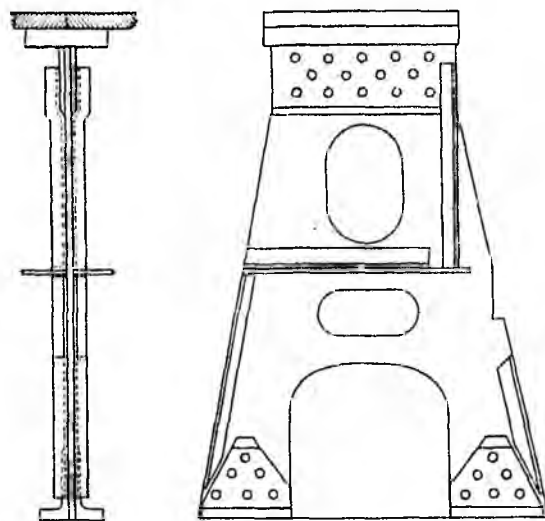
Plaatframe uit 1" ketelplaat, constructie Vickers.
